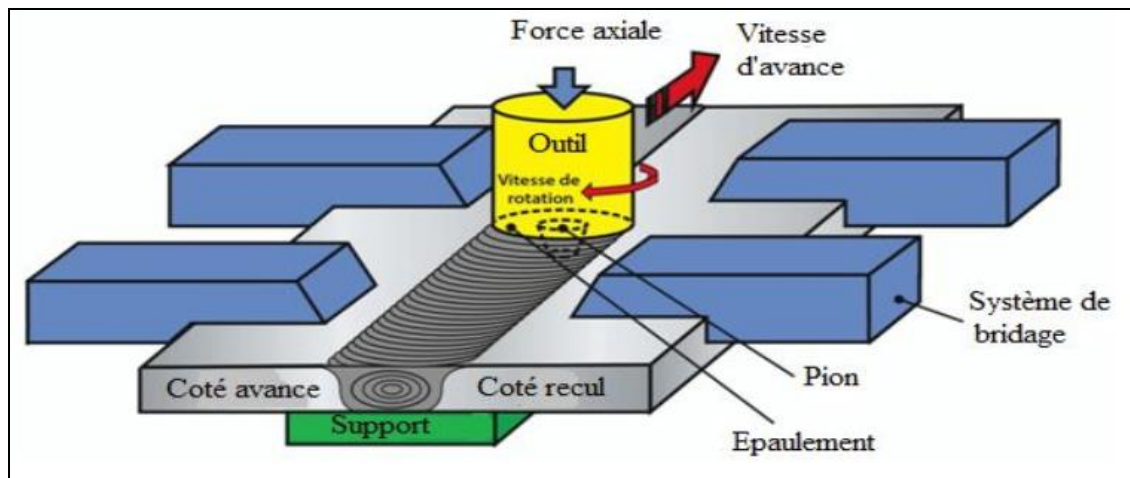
Schéma montrant les principales composantes de l'outillage en soudage par friction malaxage (FSW) [14].
